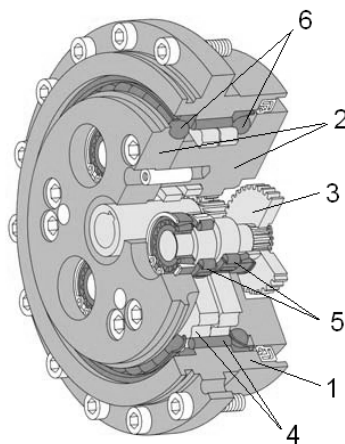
Вариант трехвальной схемы планетарно-цевочного редуктора 2K-V фирмы «Nabtesco»: 1 – корпус; 2 – водило; 3 – эвольвентный сателлит быстроходной ступени; 4 – эпициклоидный сателлит и цевка внецентроидного внутреннего цевочного зацепления; 5 – цилиндрические роликовые подшипники; 6 – шарики радиально-упорных совмещённых опор качения
